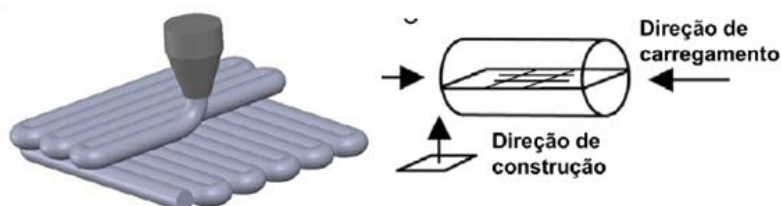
Deposição de filamento e direção de carregamento. Fonte: Lovo & Fortulan (2016).
